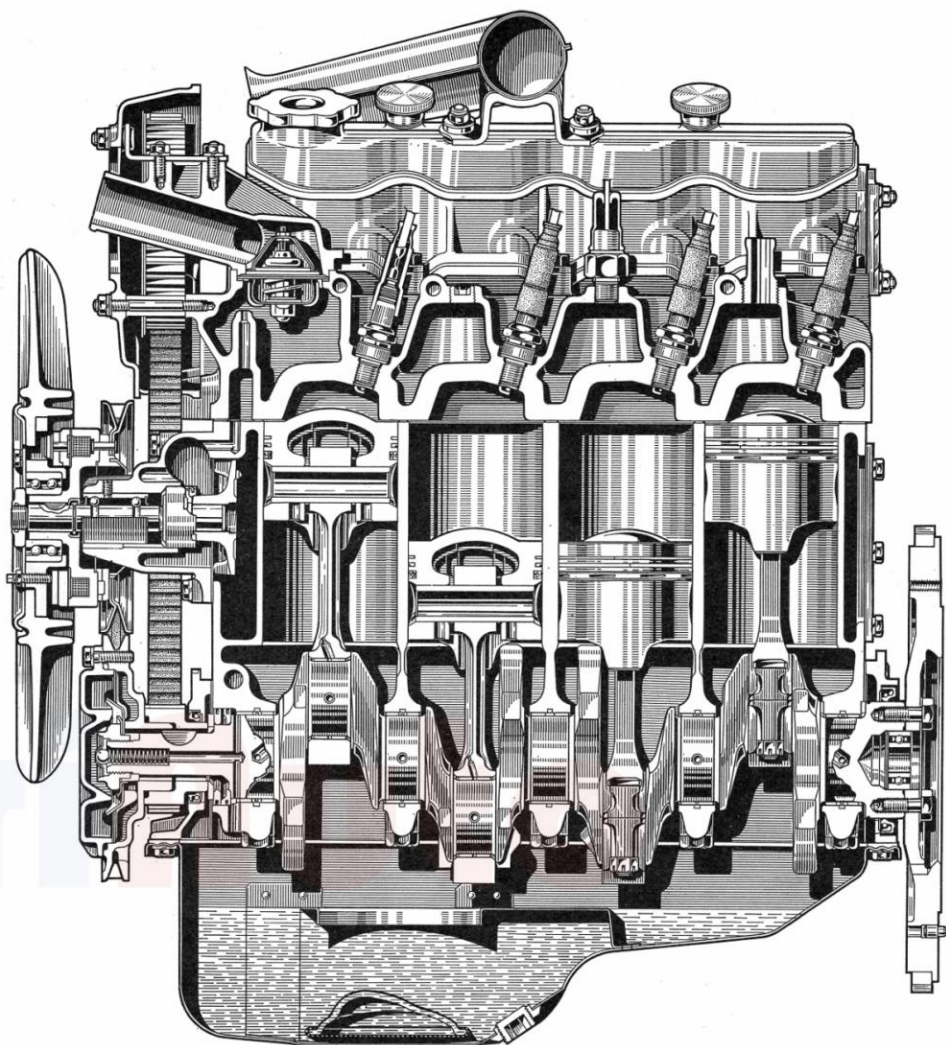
Längsschnitt durch die Zylinder des Motors.
